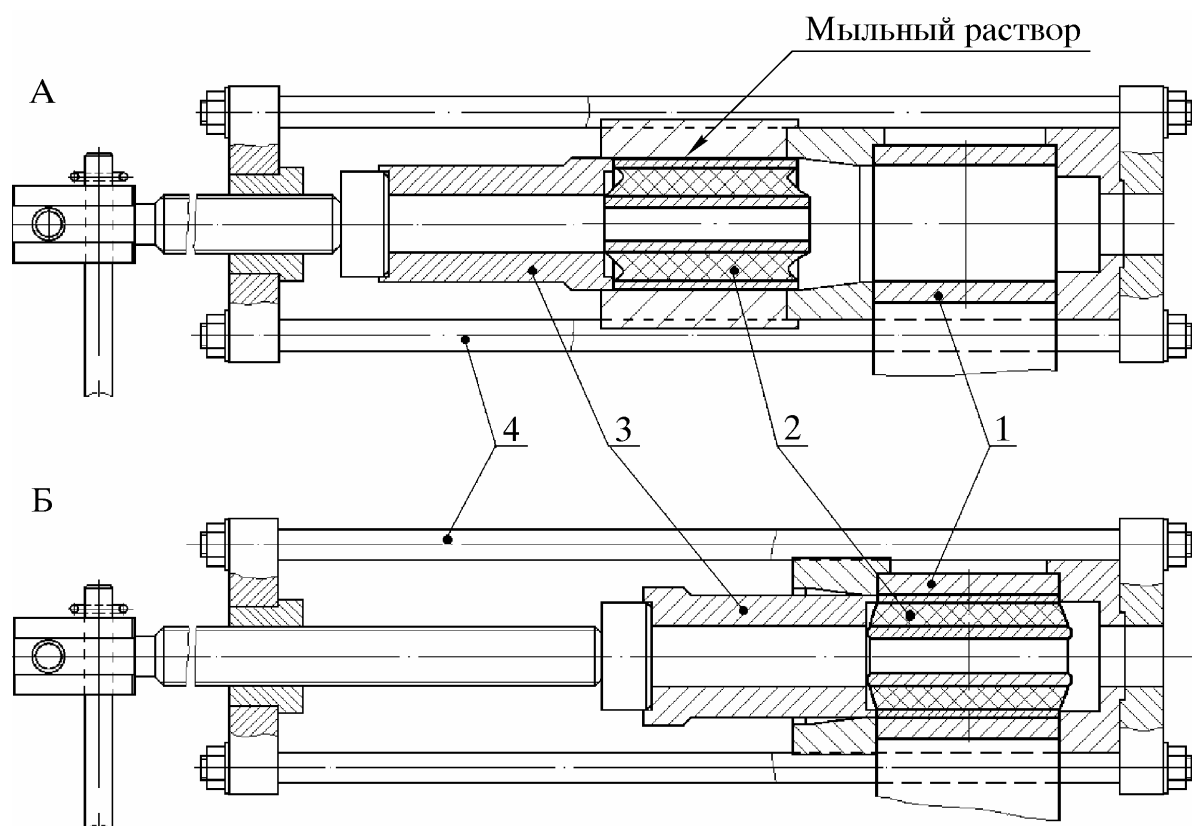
Запрессовка резинометаллического шарнира в отверстие наконечника штанги стабилизатора:
